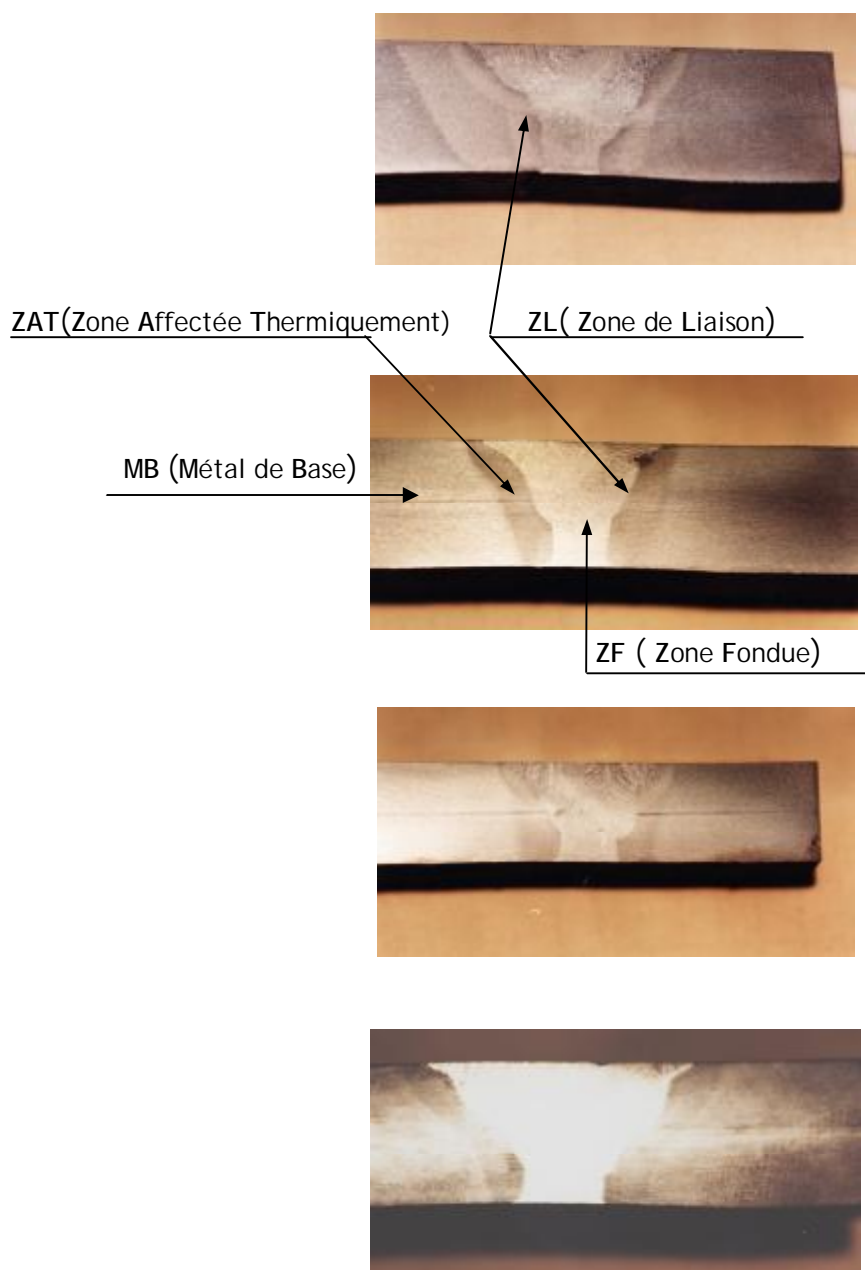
Macrographie des joints soudés pour les échantillons
